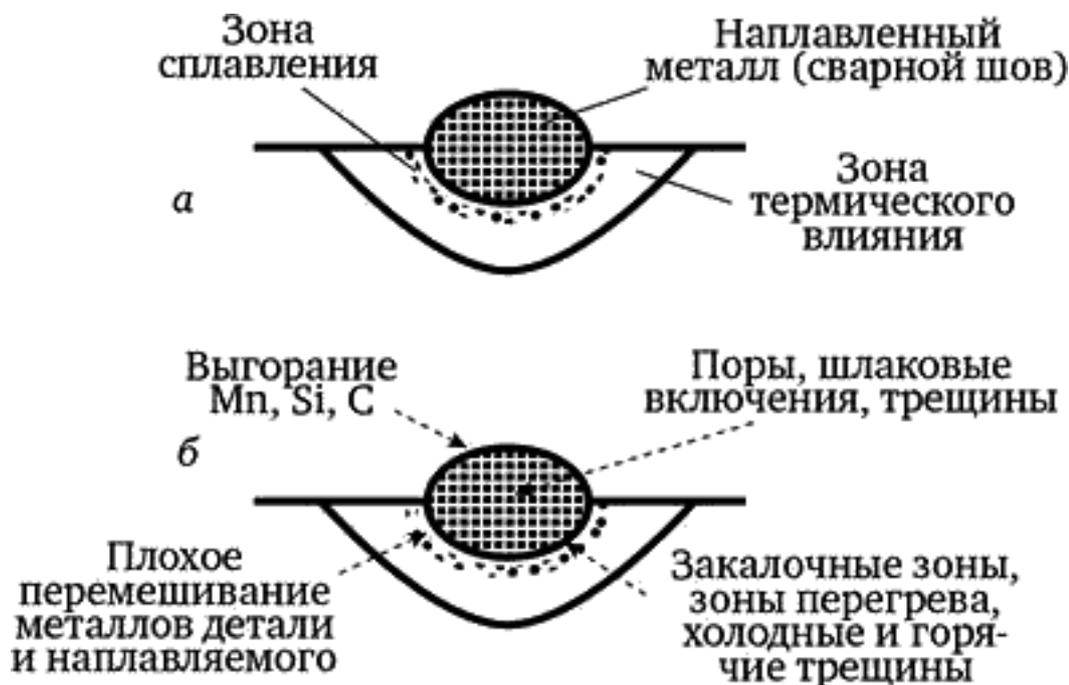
Зоны сварного шва (а) и возможные дефекты в нем (б)
